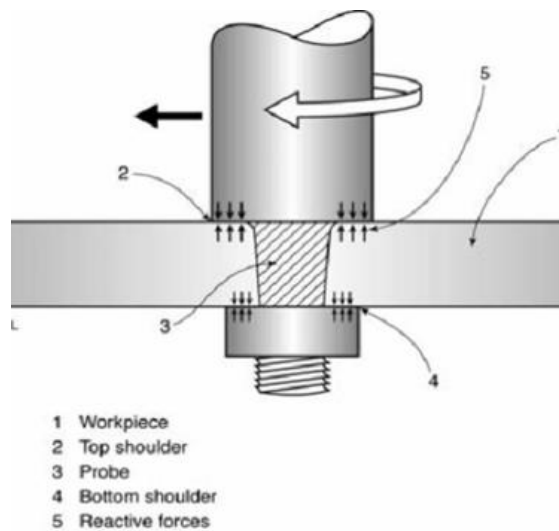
Schéma du principe de soudage par friction malaxage avec outil à double-épaulement [11]
